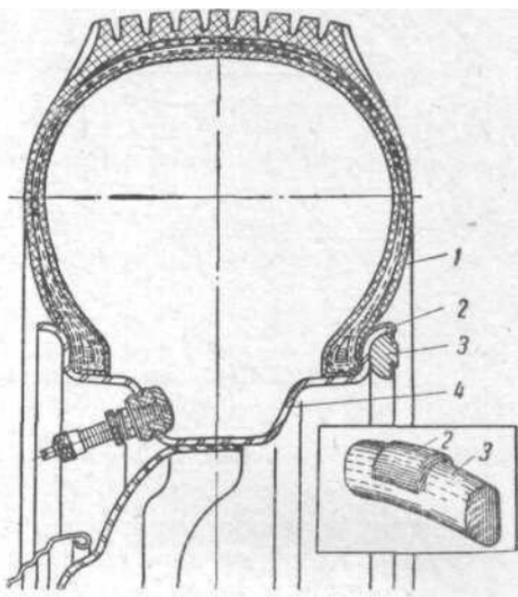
Крепление балансирующего грузика на ободе колеса:
